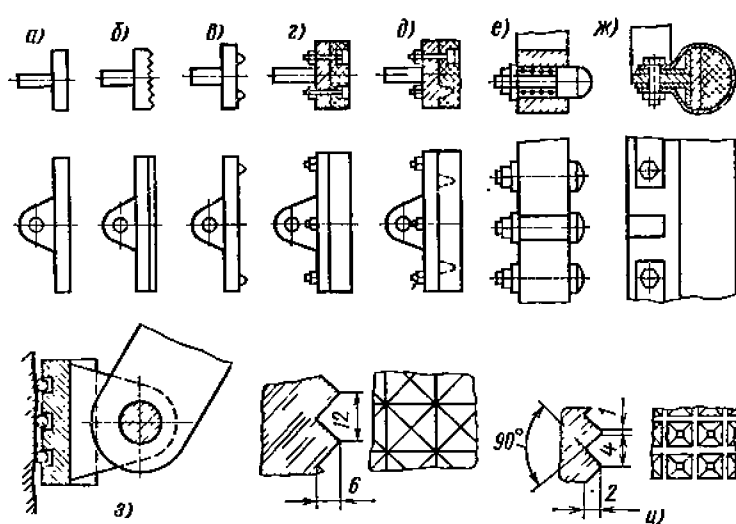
Конструкция захватных органов зажимных ГУ: а — гладкая металлическая; б — с насечкой; в — с шипами; г — с накладкой из толстой резины; д — то же, с шипами внутри; е — в виде кулачков на пружине; ж — с накладкой из пористой резины, обтянутой конвейерной лентой; з — с накладкой из стальных канатов; и — профильные насечки поверхности контакта
